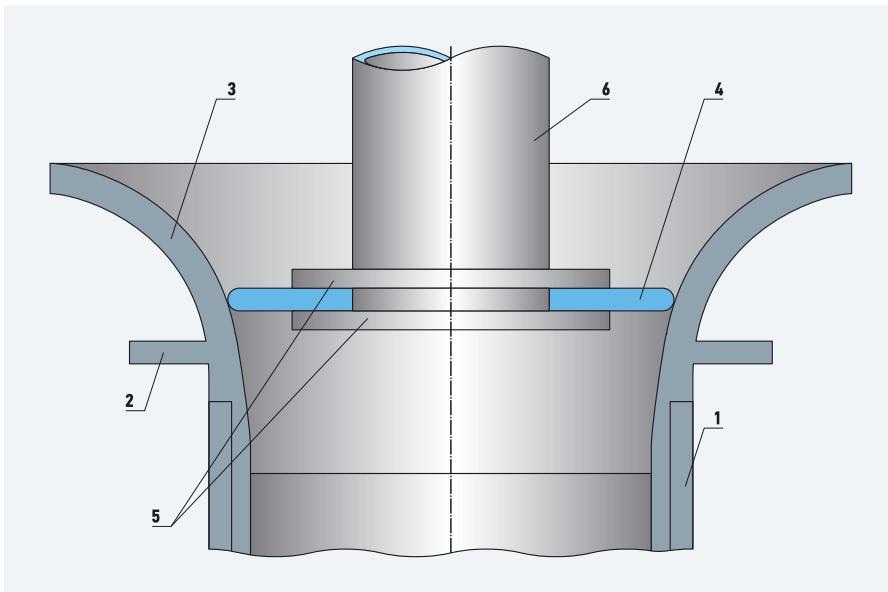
Гипотетическая спускная арматура с коноидальным входным участком спускного отверстия (1 — корпус; 2 — опорный диск корпуса; 3 — коноидальный насадок; 4 — эластичный клапан; 5 — диски на переливной трубе; 6 — переливная труба)
